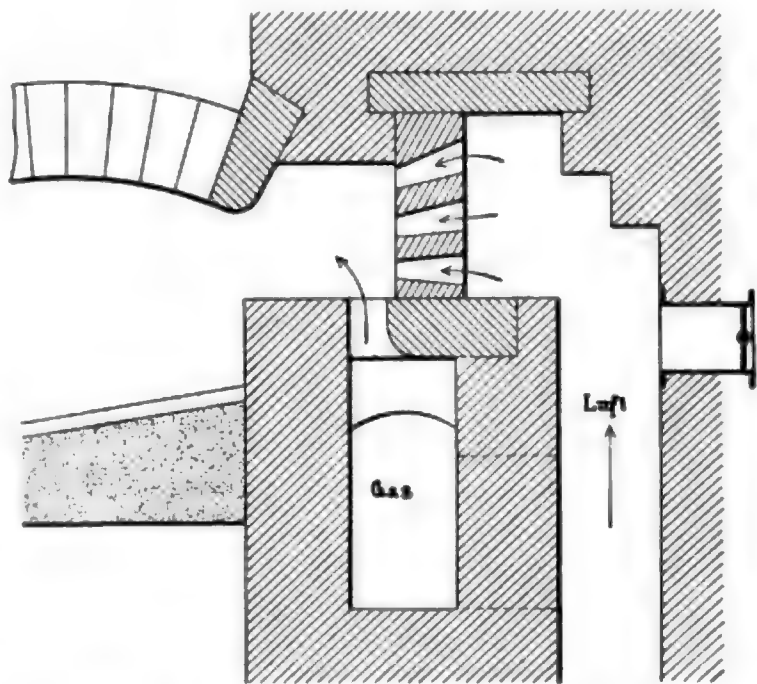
Gasrohrschweißofen mit Halbgasfeuerung.
